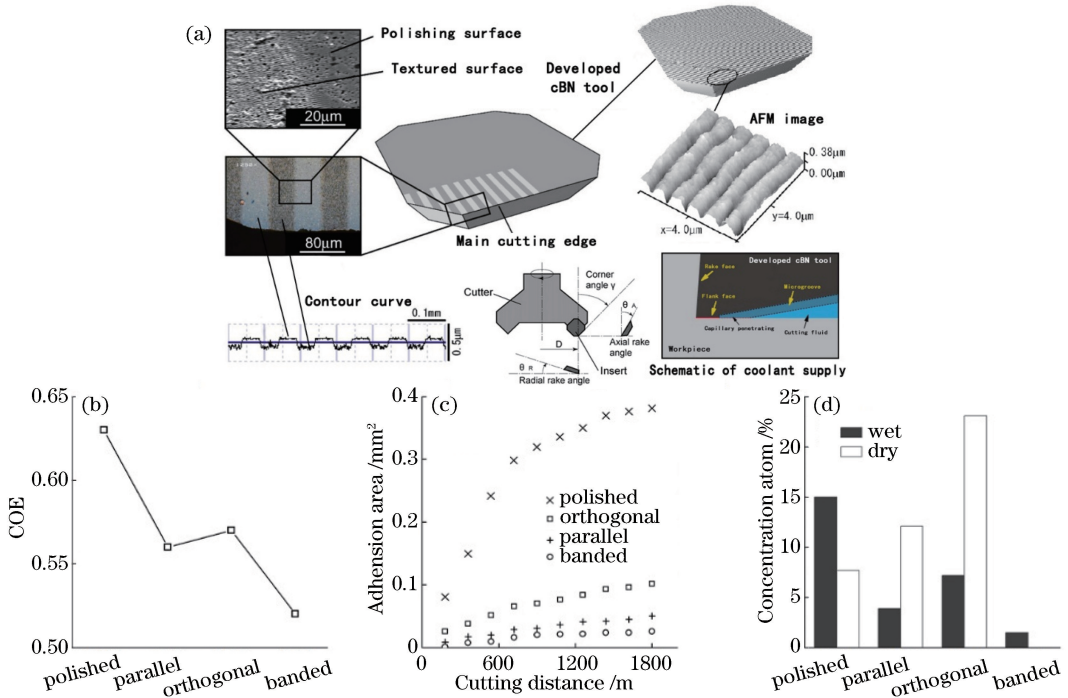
飞秒激光诱导表面微结构 CBN 刀具表面微观形貌及不同刀具在不同切削条件(干加工/湿加工)下的切削实验结果分析。(a)表面微观形貌;(b)不同结构(原始抛光表面、平行微结构、交叉微结构和带状微结构)刀具的摩擦因数;
